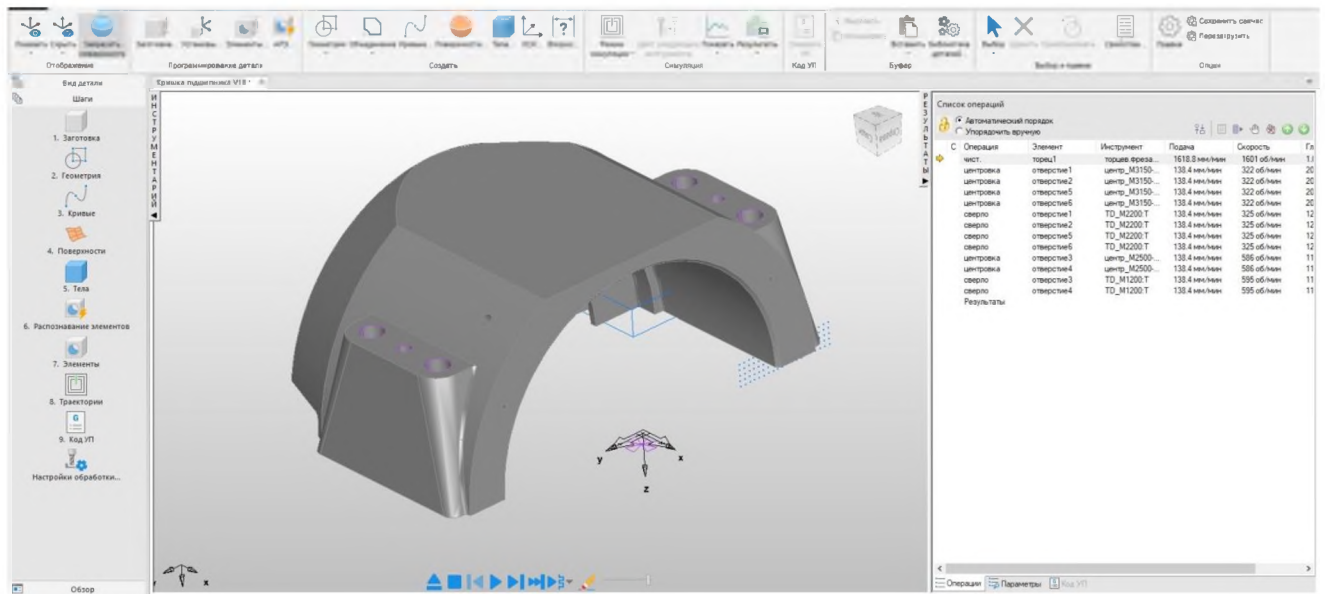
Етапи обробки деталі «Корпус підшипника»
